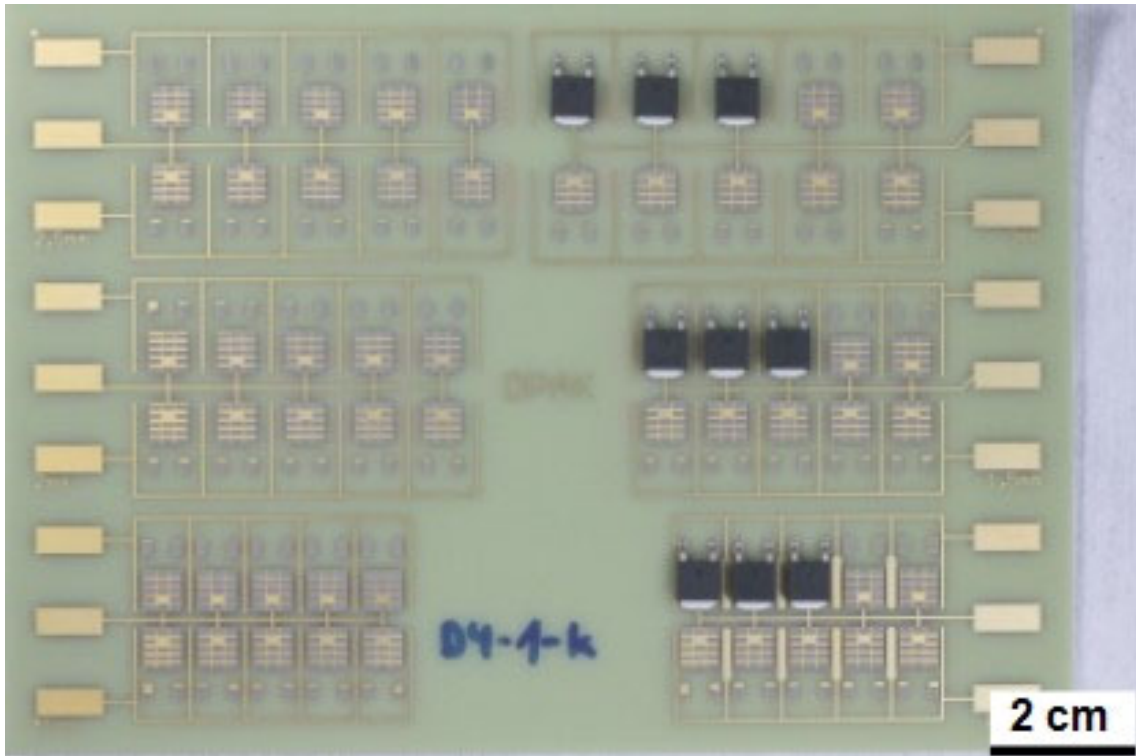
Hochvolt-SIR-Test Board, gedruckt und teilbestückt.
